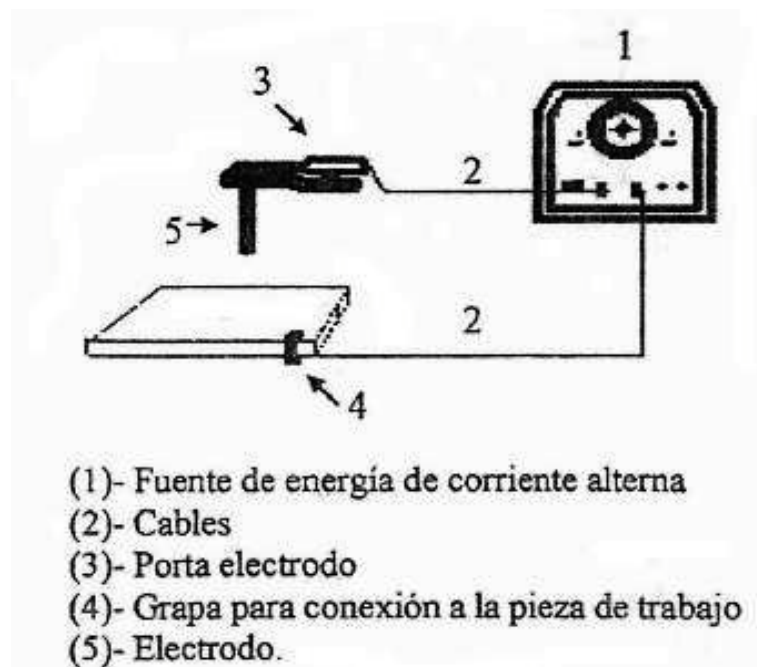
Circuito básico de soldadura en una maquina de corriente alterna.
